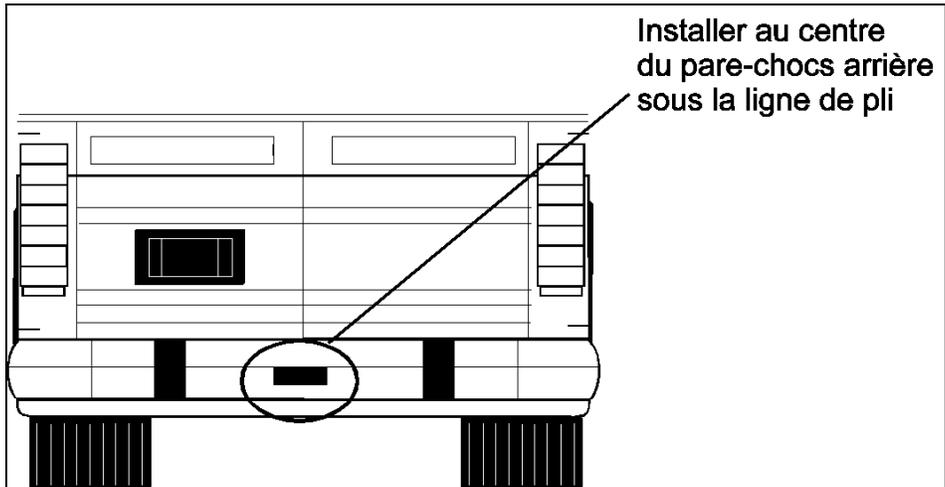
VUE ARRIÈRE D'UNE CARROSSERIE D'AUTOCAR XL
